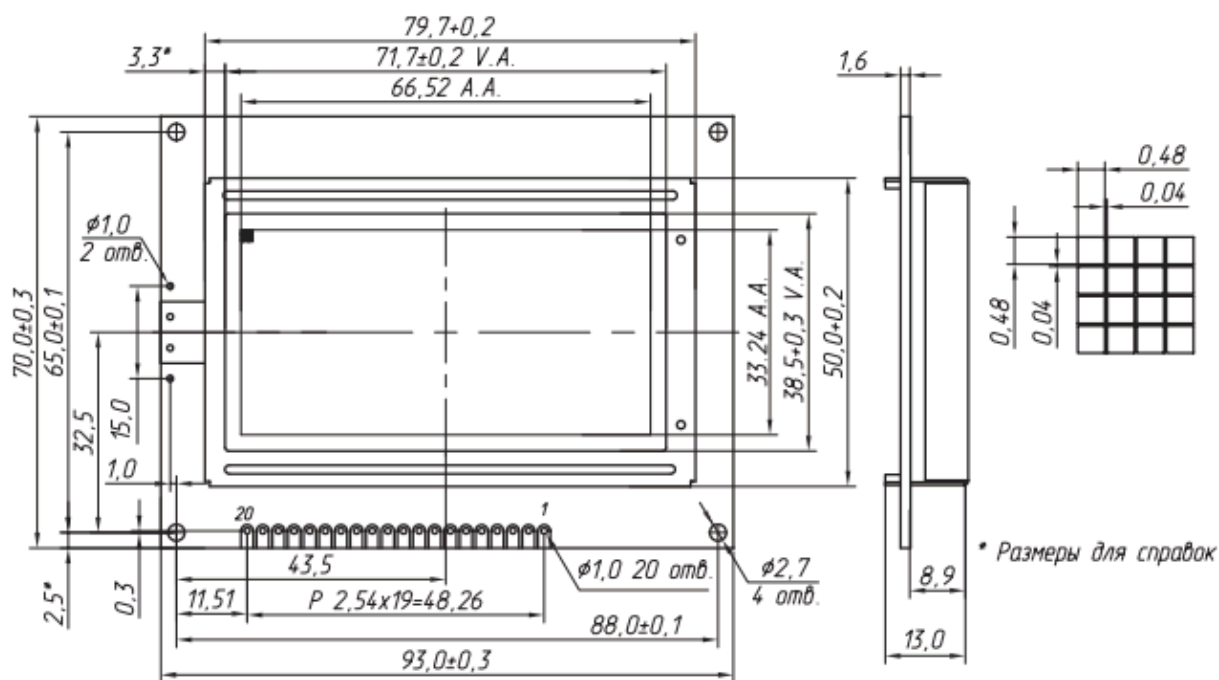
Габаритные размеры МТ-12864J-23FLW-3V0-890
